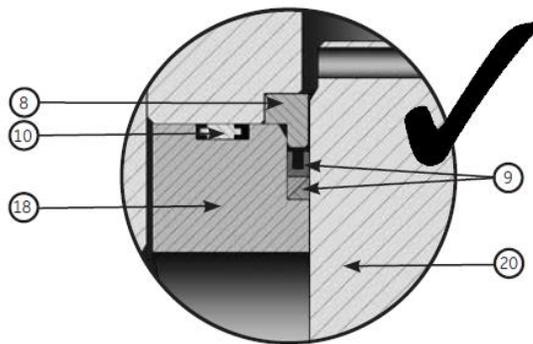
В – Надлежащая установка уплотнительного кольца: угол 90° нижнего упорного кольца направлен к экструзионному зазору
